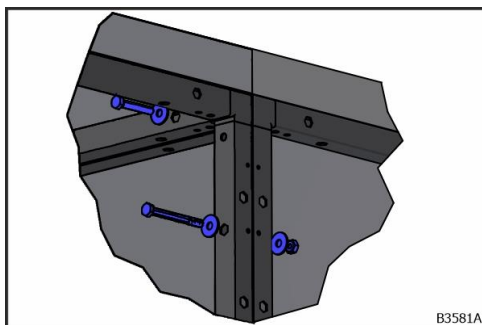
Sechskantschraube, Scheiben und Sechskantmutter
